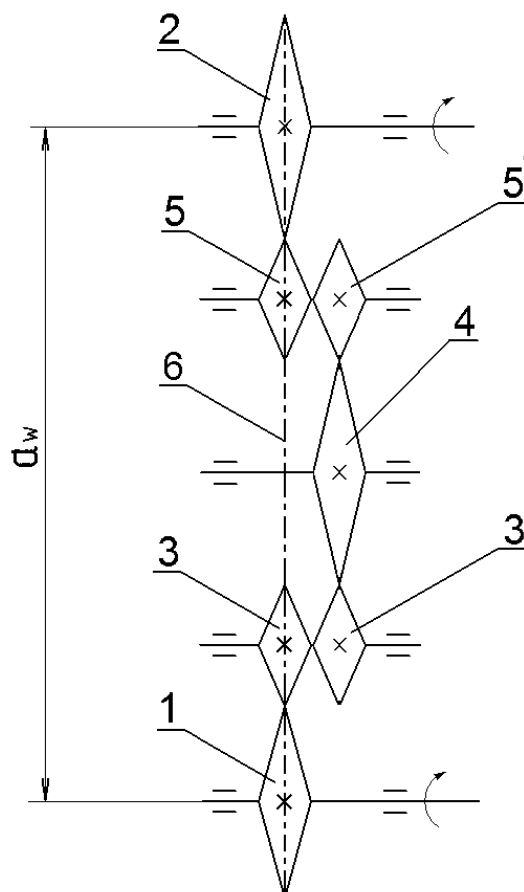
Схема зубчато-цепной передачи с зубчатой цепью
